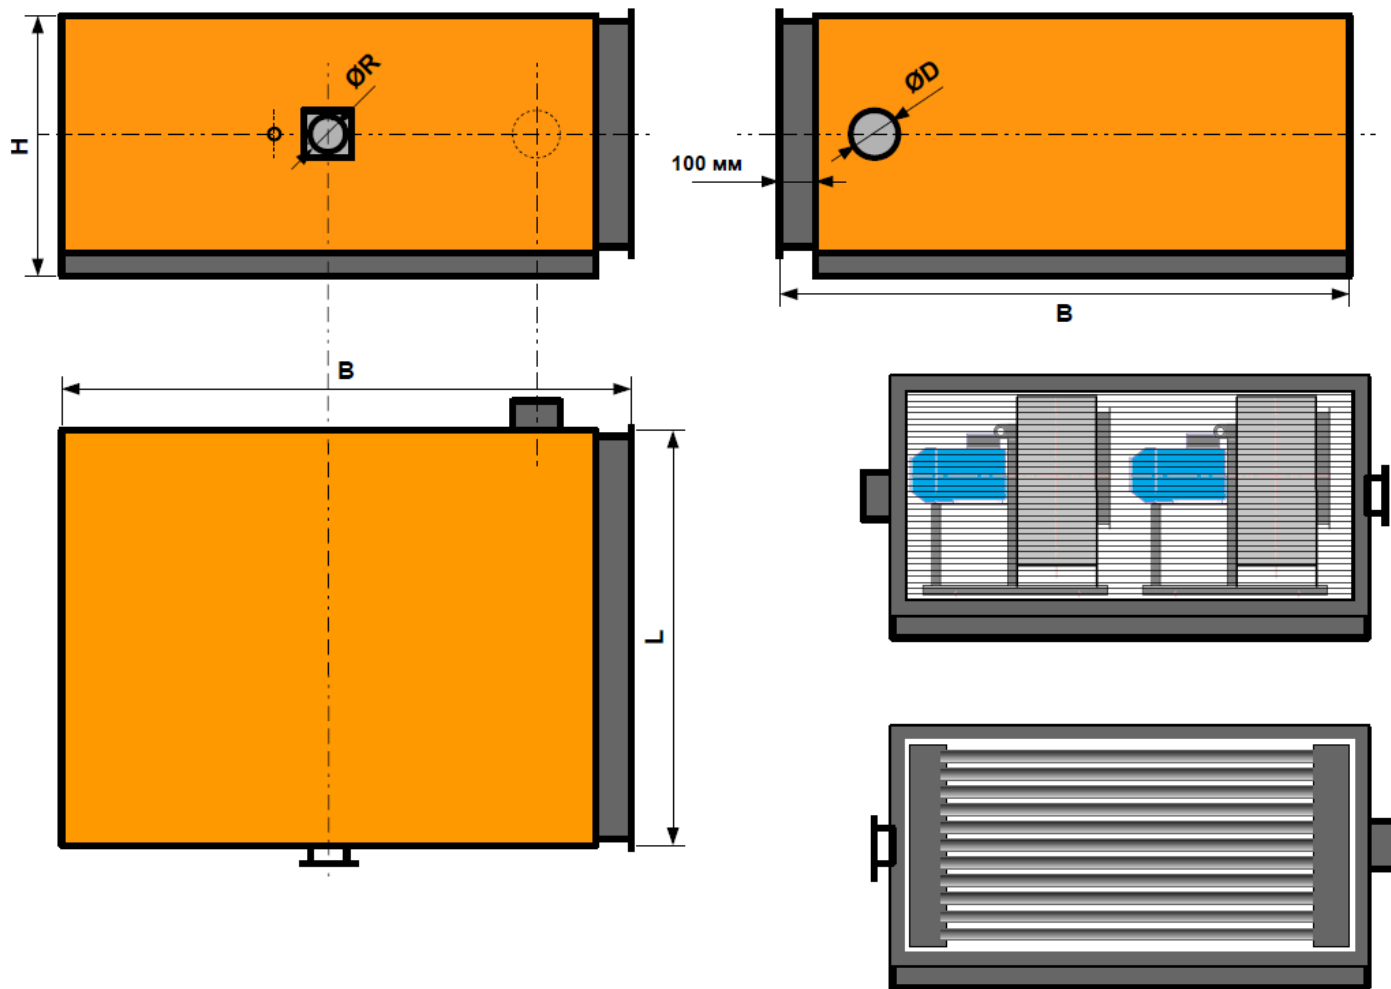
Габаритные размеры воздухонагревателей (теплообменников) серий НТ-К
